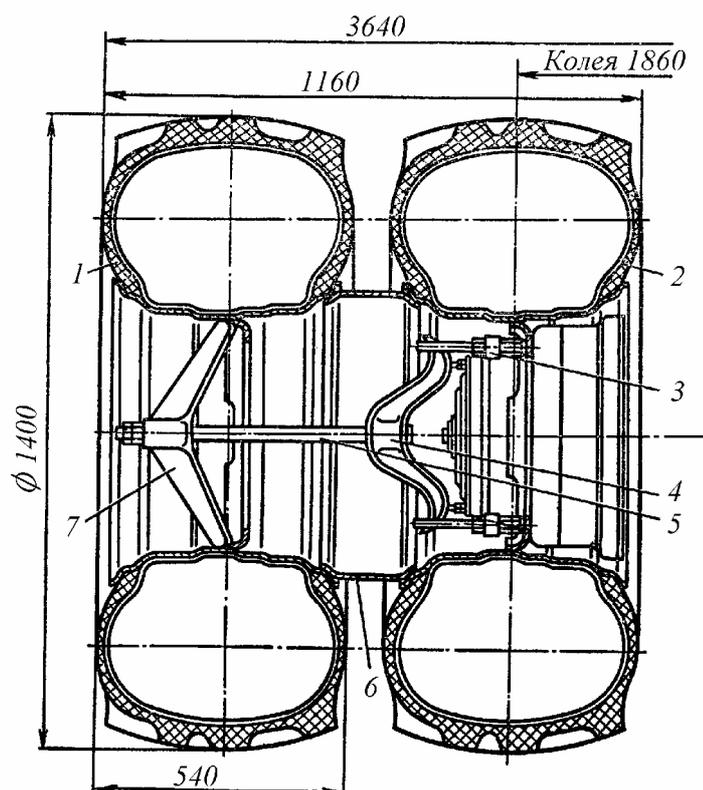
Приспособление для сдвигания колес трактора Т-150К:
